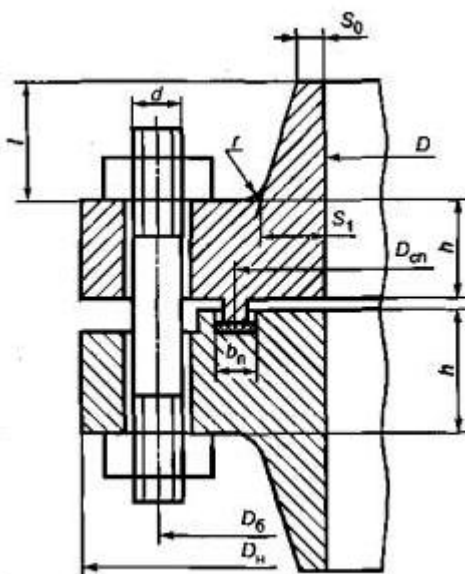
Фланцевое соединения с приварными встык фланцами с гладкой уплотнительной поверхностью типа шип - паз.
